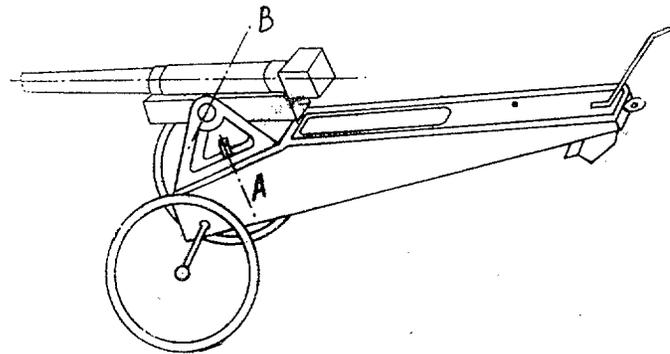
^a—Montaje o cureña monomástil: A, eje de puntería en dirección; B, eje de puntería en altura.
